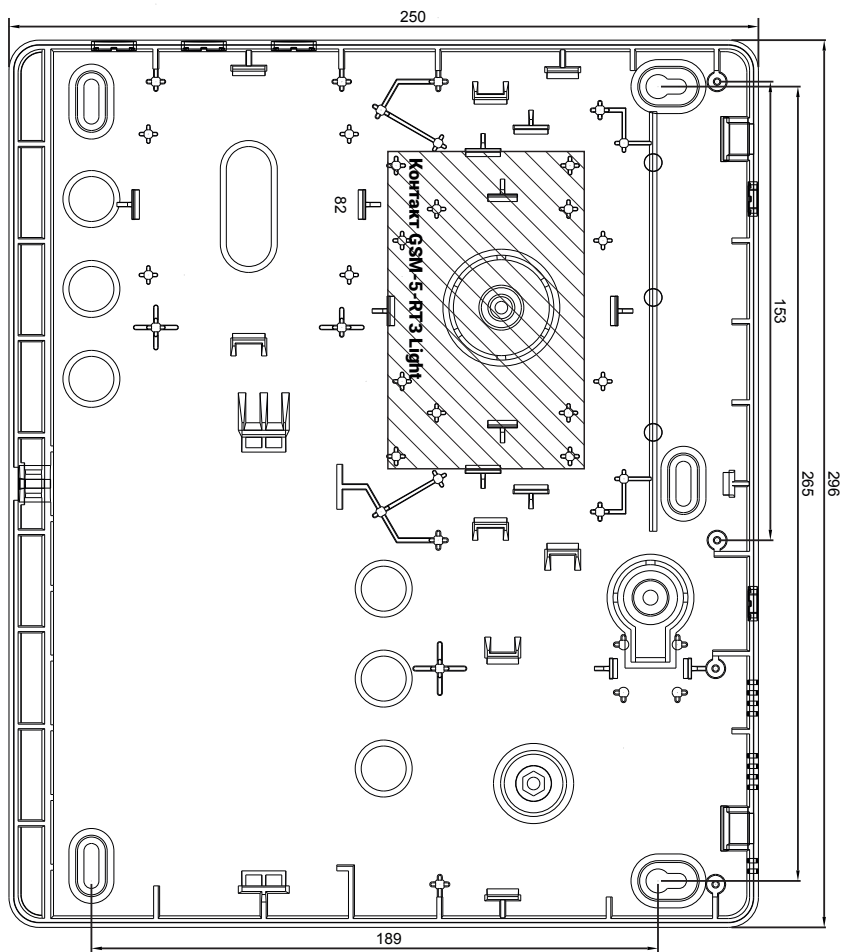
Установка панели в корпус «Контакт» 7 Ач
